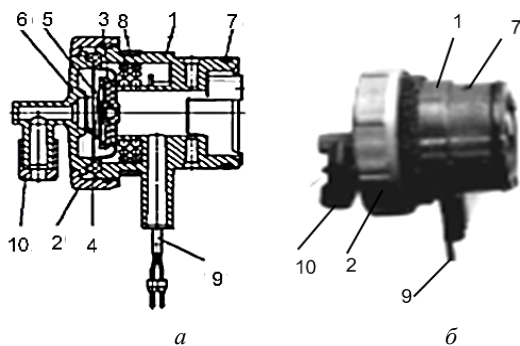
Схема (а) и общий вид (б) блока продувки в сборе:
